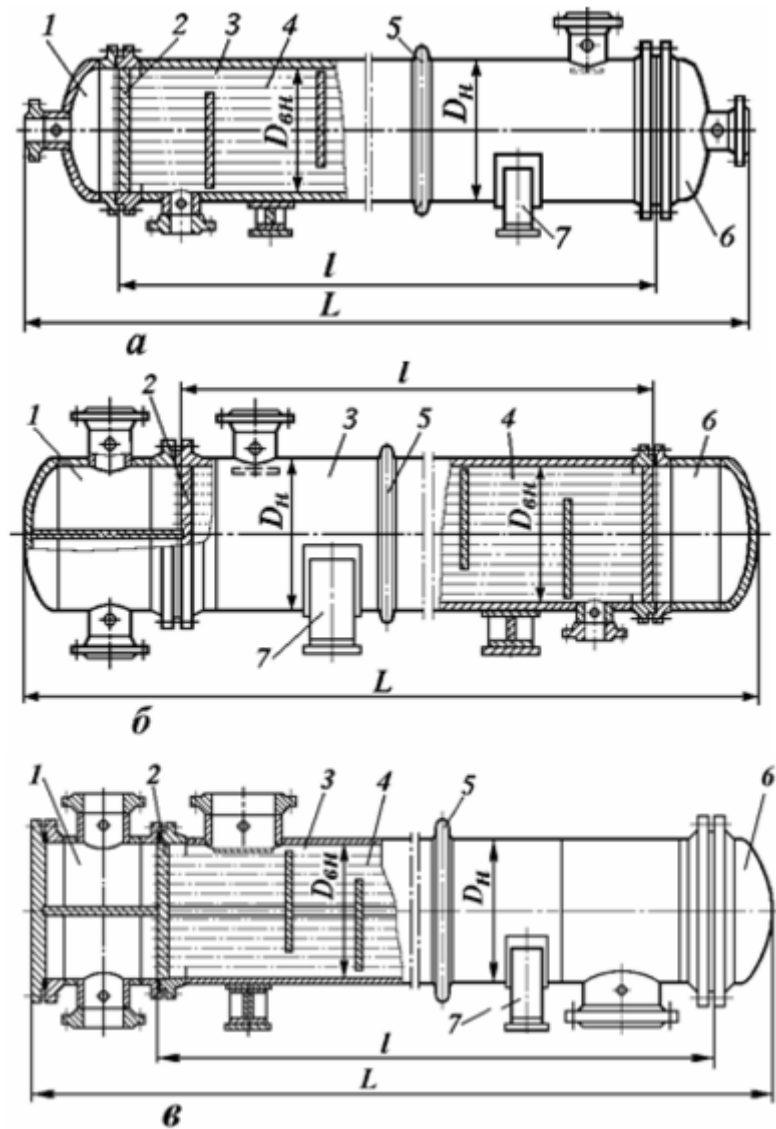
Кожухотрубні горизонтальні теплообмінники напівжорсткої конструкції: а - одноходовий; б - багатоходовий з двома еліптичними кришками; в - багатоходовий з плоскою кришкою; 1 - розподільна камера; 2 - трубна решітка; 3 - корпус - кожух; 4 - трубчатка; 5 - компенсатор температурний; 6 - кришка задня; 7 - опора.
